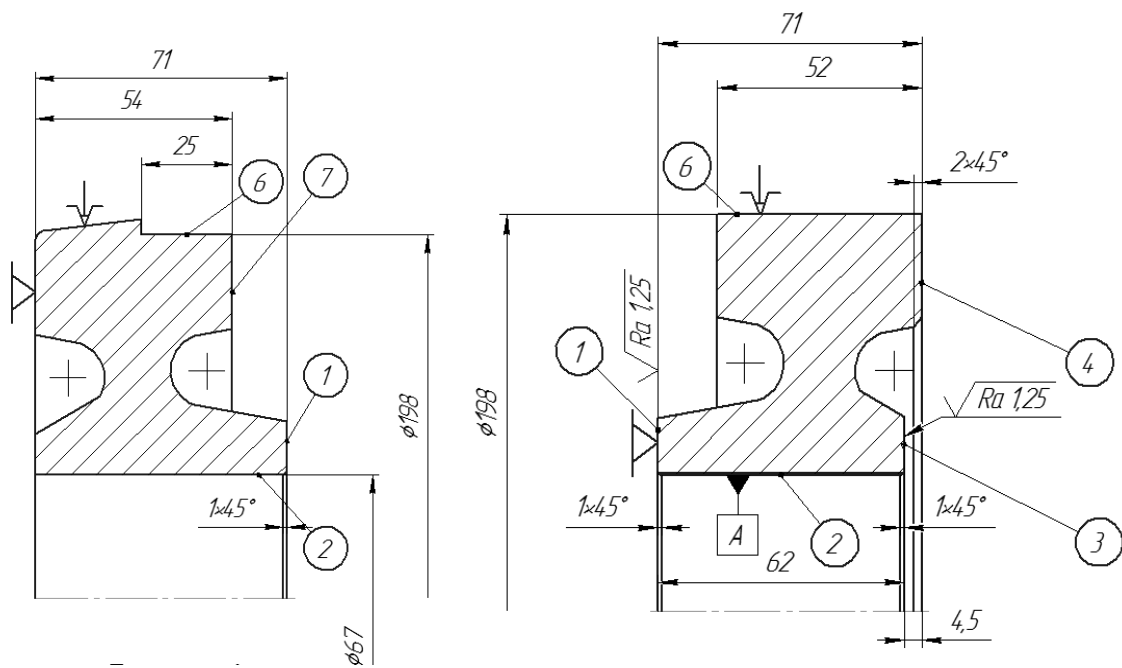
Поверхности детали «Колесо зубчатое»
